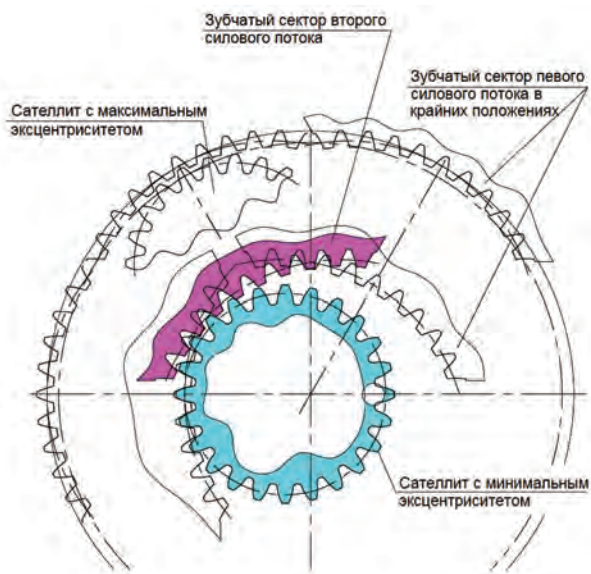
Схема планетарной плавно регулируемой передачи для случая, когда число зубьев заготовки для изготовления секторов меньше максимального условного числа зубьев центрального зубчатого колеса
